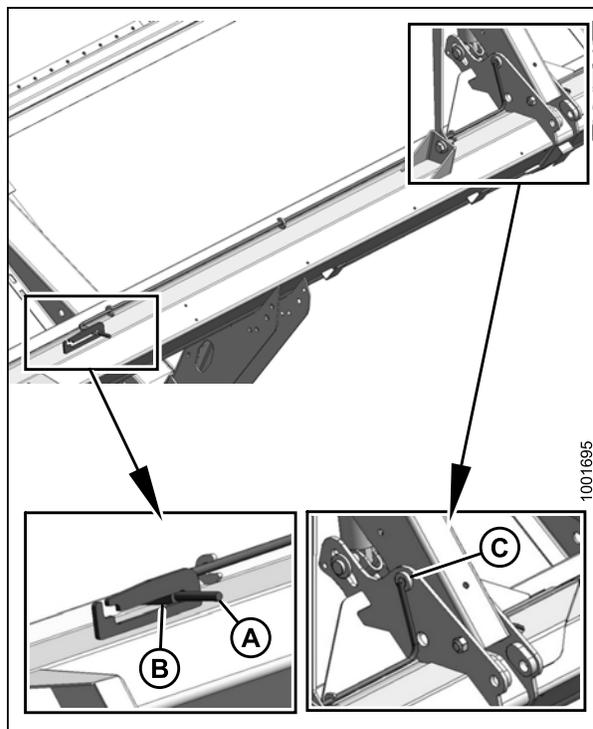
Предохранительный упор мотовила — центральный рычаг
